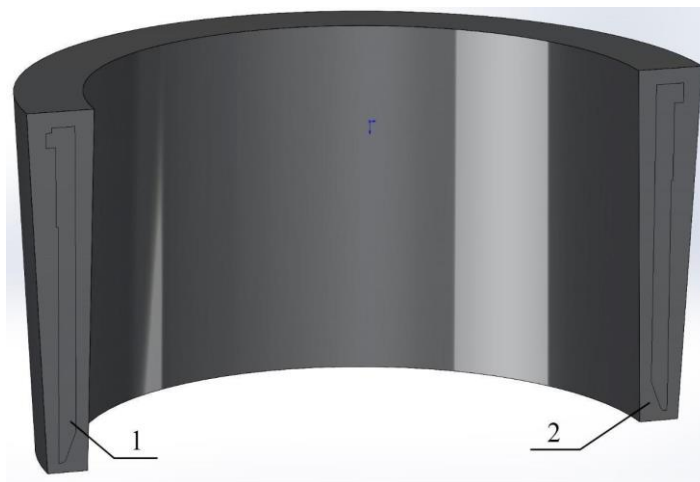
Модель виливка деталі «втулка»: 1 – модель деталі; 2 – модель виливка
